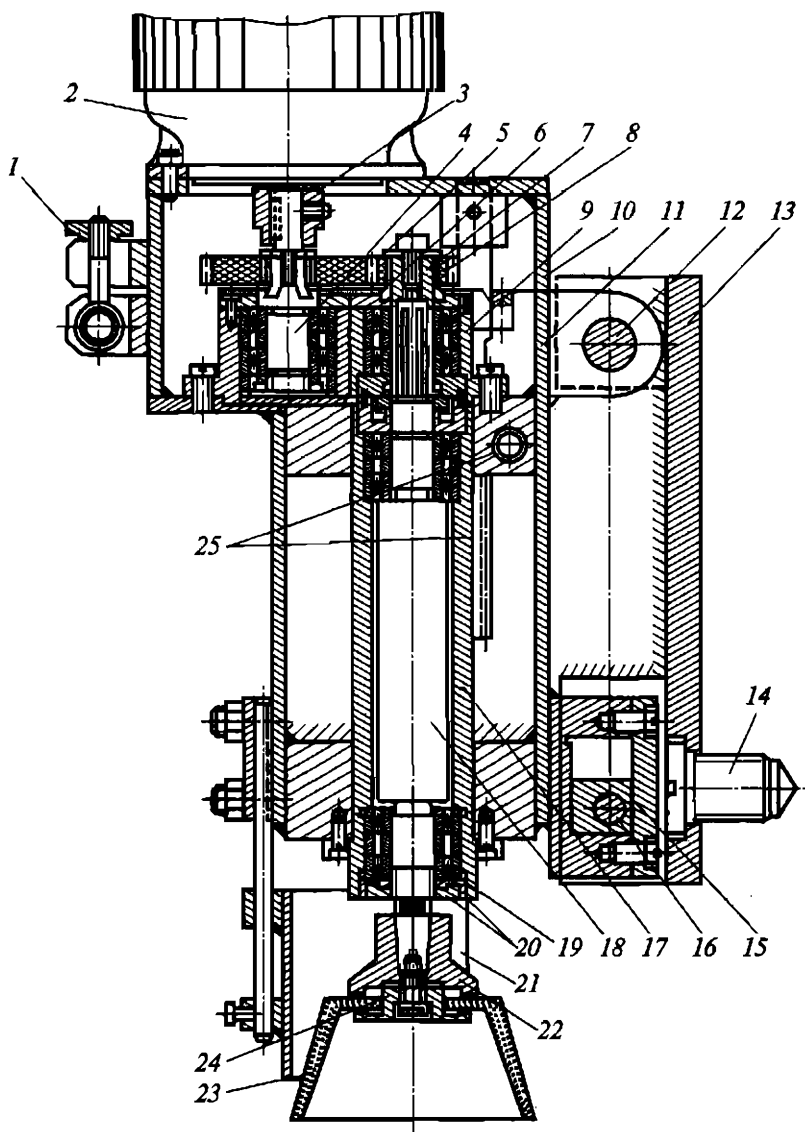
Стационарное приспособление для восстановления направляющих шлифованием или фрезерованием:
